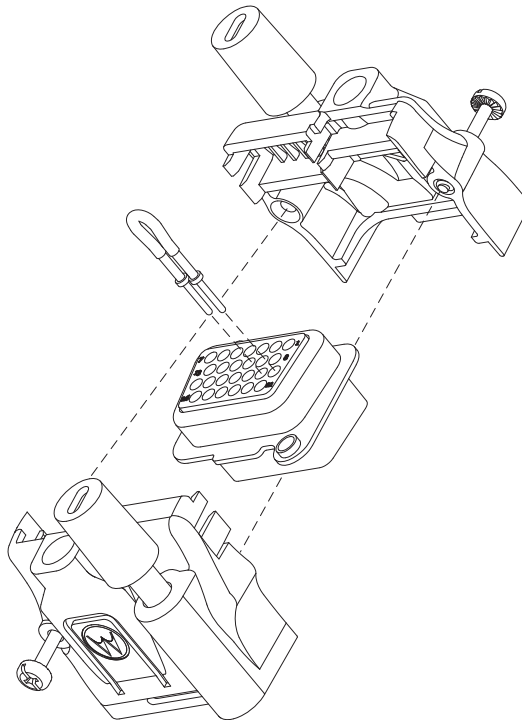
Visão Detalhada do Conjunto do Conector para Acessórios (HLN6863_)
